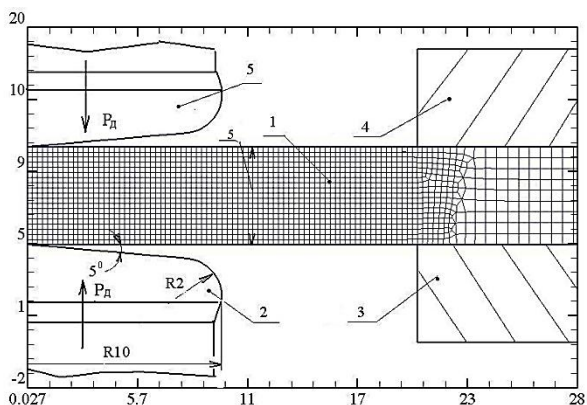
Розрахункова схема процесу видавлювання (розміри в міліметрах)
